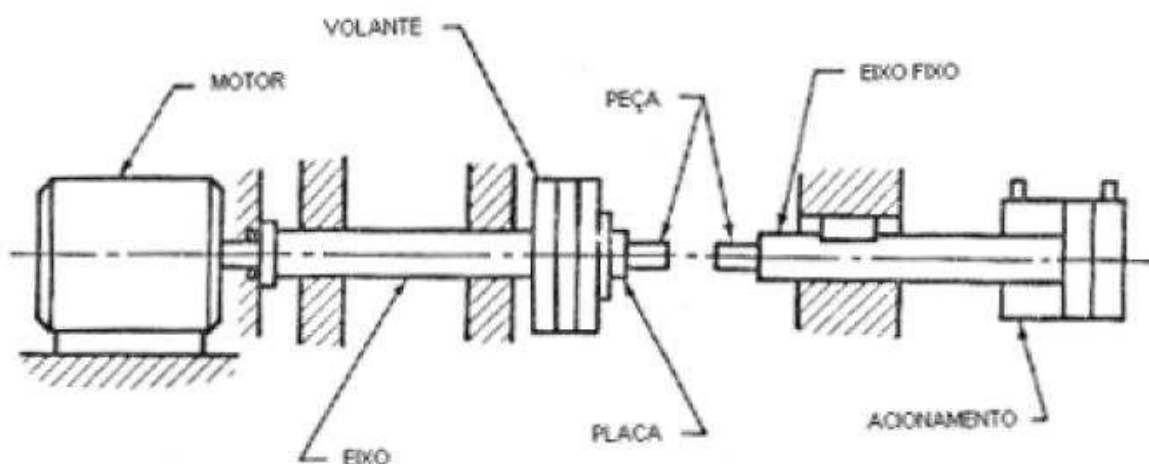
Equipamento de soldagem por fricção inercial– SILVA (2011)
